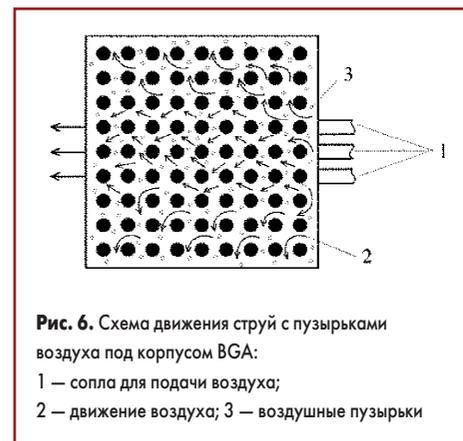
Схема движения струй с пузырьками воздуха под корпусом BGA:
